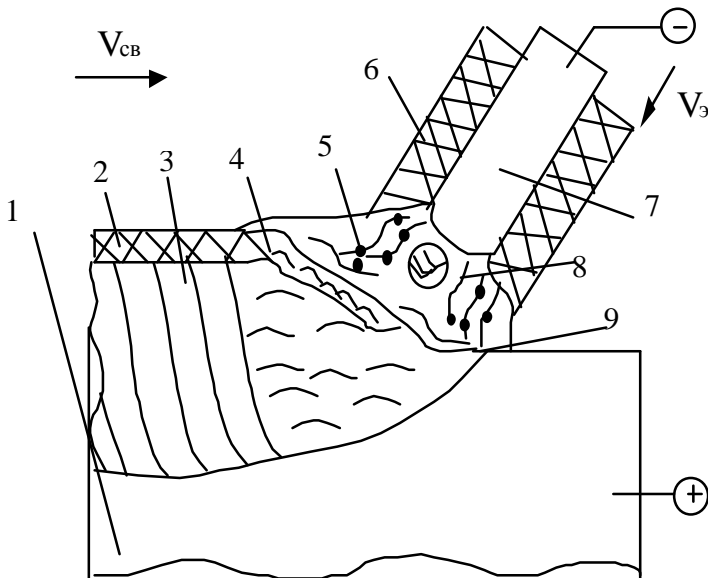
Схема сварки металлическим покрытым электродом (прямая полярность)
